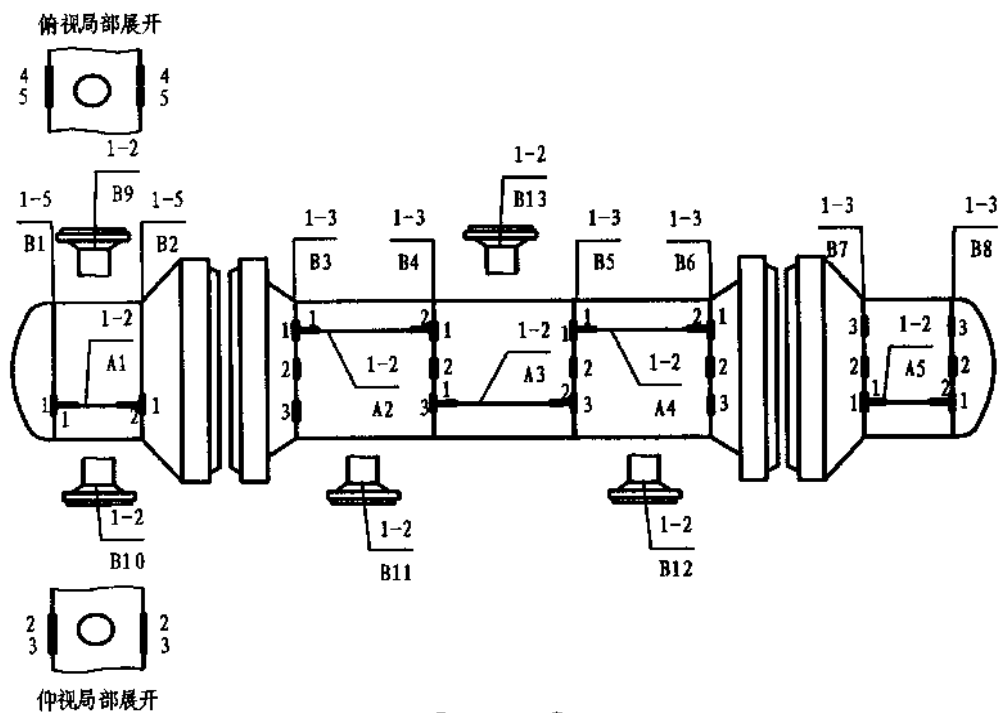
焊缝局部检测部位图 (整体图)
